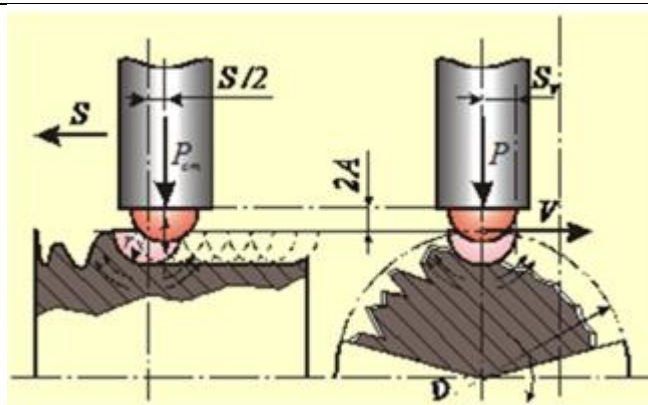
Схема поверхневого пластичного деформування при ультразвуковій зміцнювальній обробці
